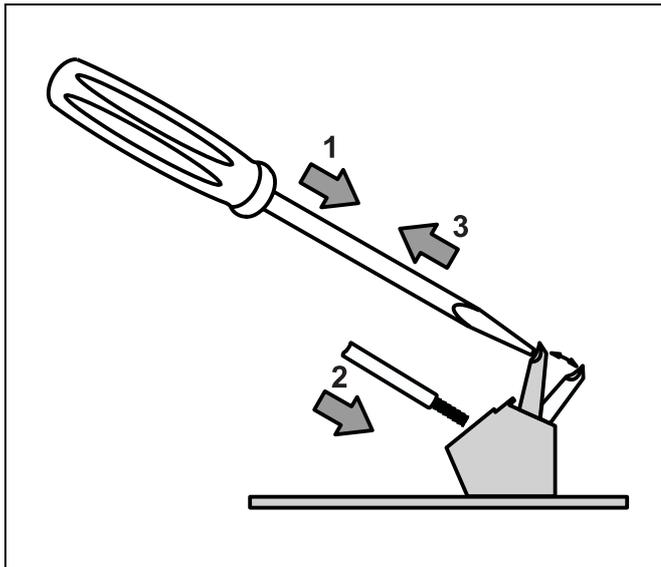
Einführung der Kabel mit schraubenlosen Federklemmen
